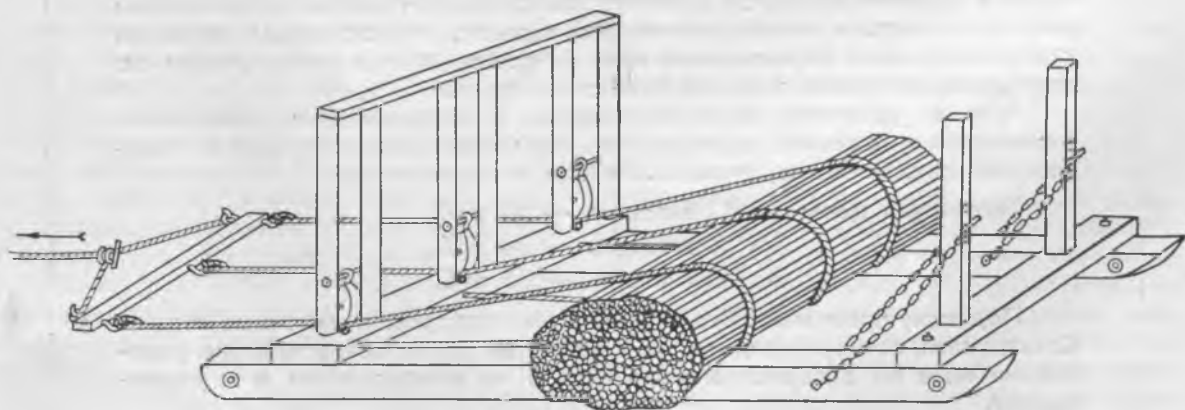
Схематический чертеж станка для прессования и увязки сучьев.
